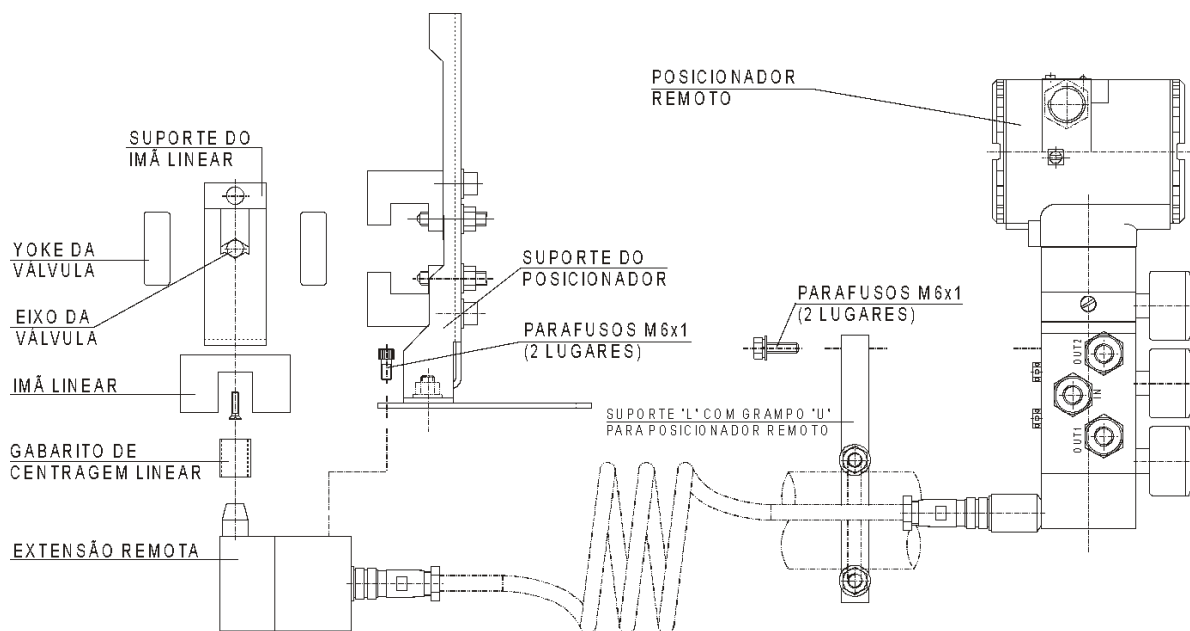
Posicionador em Atuador Linear com Sensor de Posição Remoto
